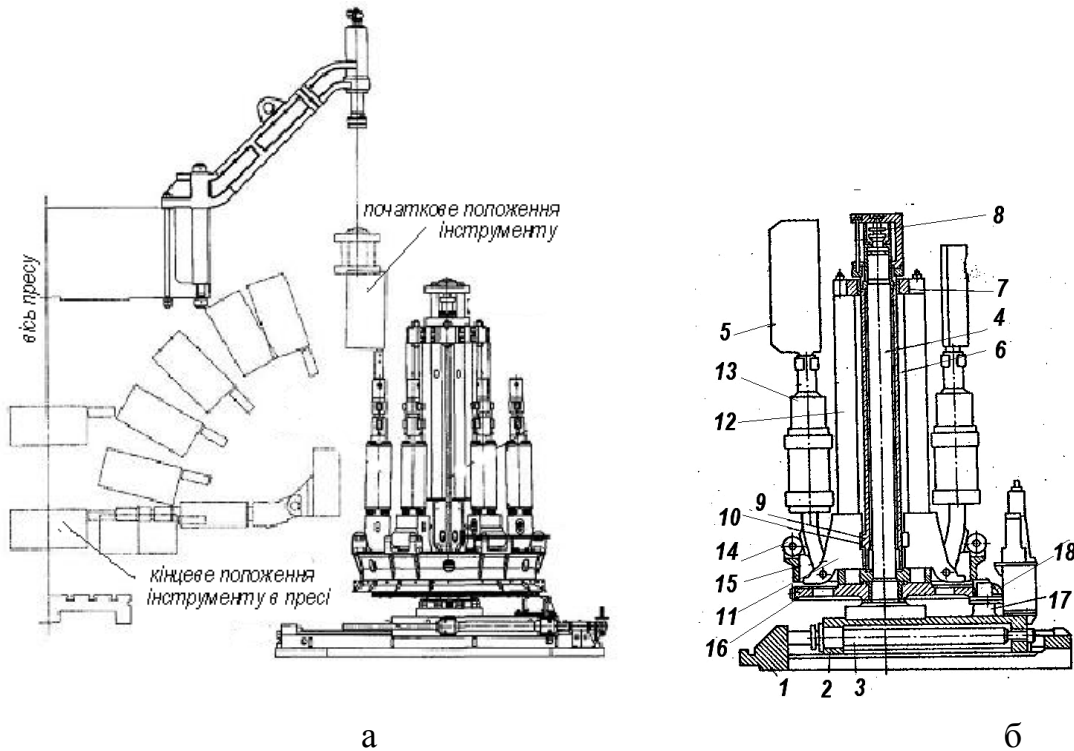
Загальний вигляд (а) та принципова схема (б) інструментального маніпулятора з шістьма штангами
